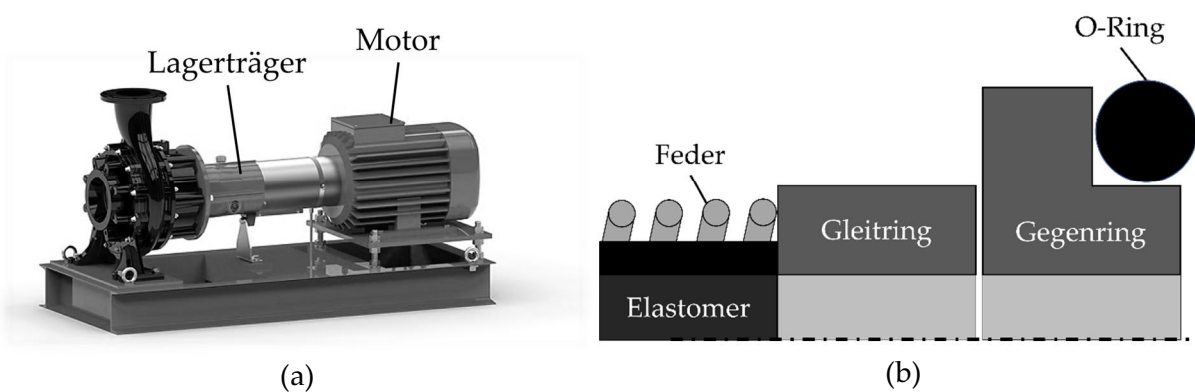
(a) Lagerträgerpumpe mit Lagerträger und Motor; (b) Bauteile einer Gleitringdichtung in der Schnittansicht, bestehend aus Feder, Elastomer, O-Ring sowie Gleit- und Gegenring.
